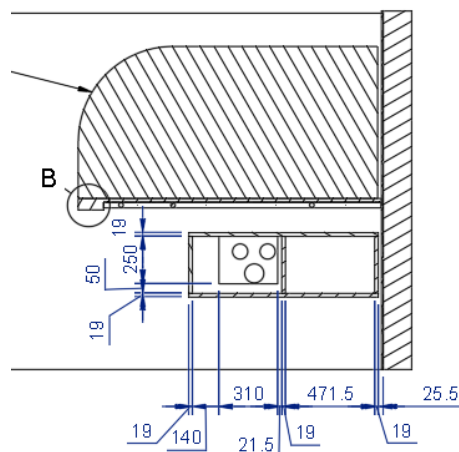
Desenho técnico de um corte que demonstra o buraco no fundo do móvel para a passagem dos canos.
